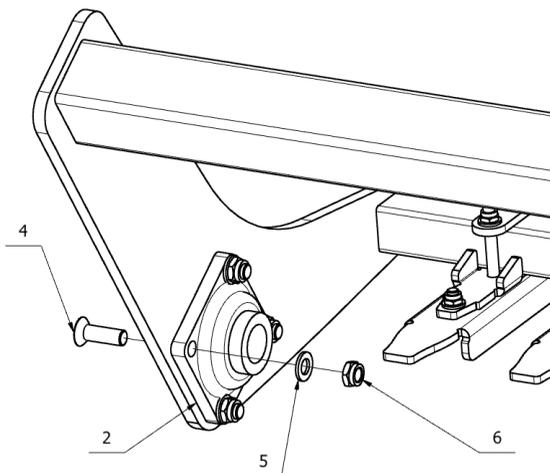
U-Profil-Walze Ø520mm – Lagermontage.
